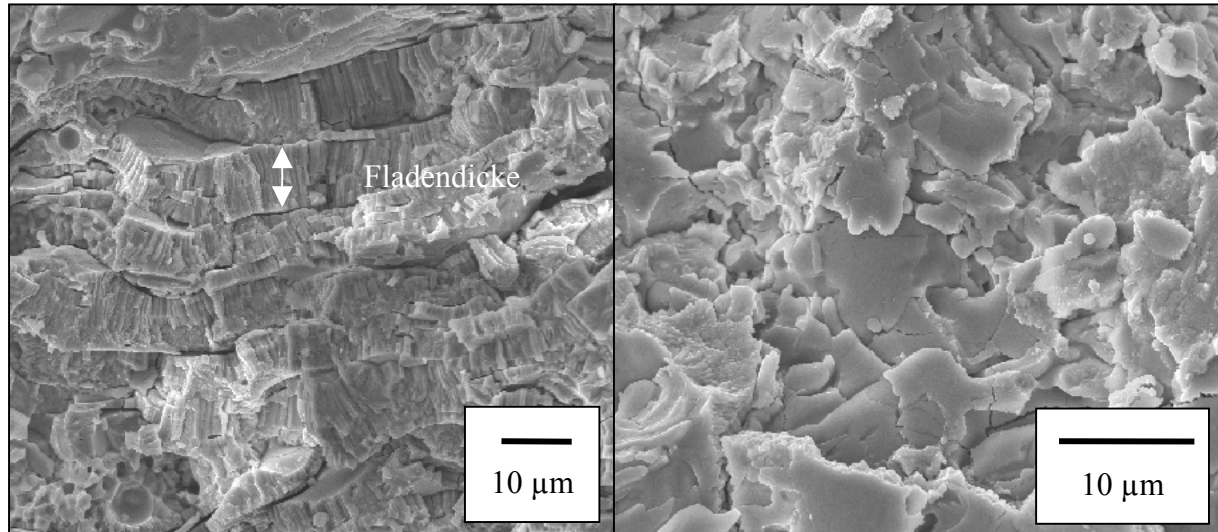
Bruchflächen einer plasmagespritzten Wärmedämmschicht senkrecht (links) und parallel (rechts) zur Spritzrichtung; /54/
